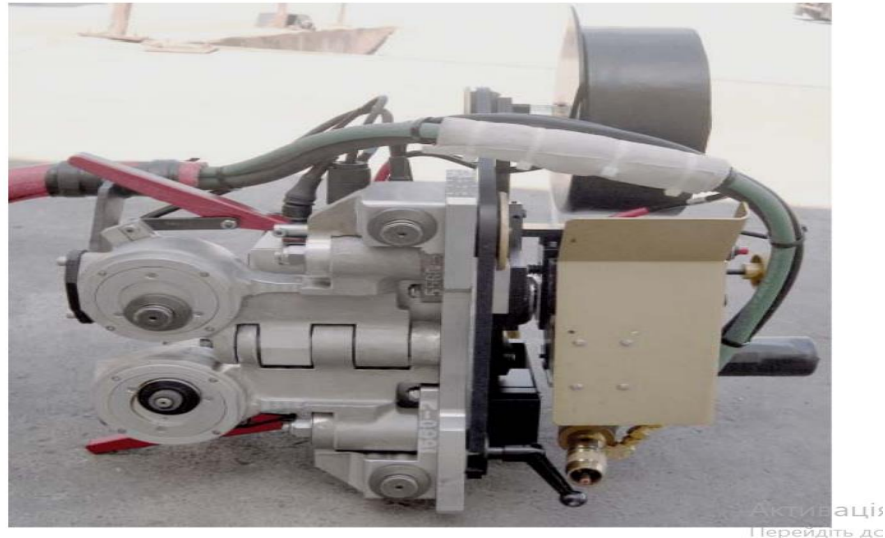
Схема зварювання, що рекомендується, головками М300-С (М300) неповоротна
